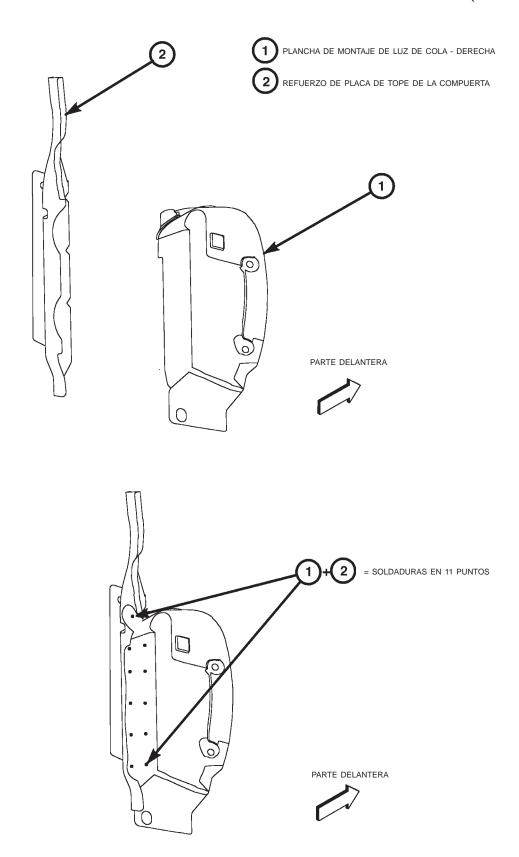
PLANCHA DE MONTAJE DE LAS LUCES DE COLA
